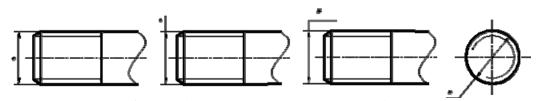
Изображение цилиндрической резьбы на стержне
